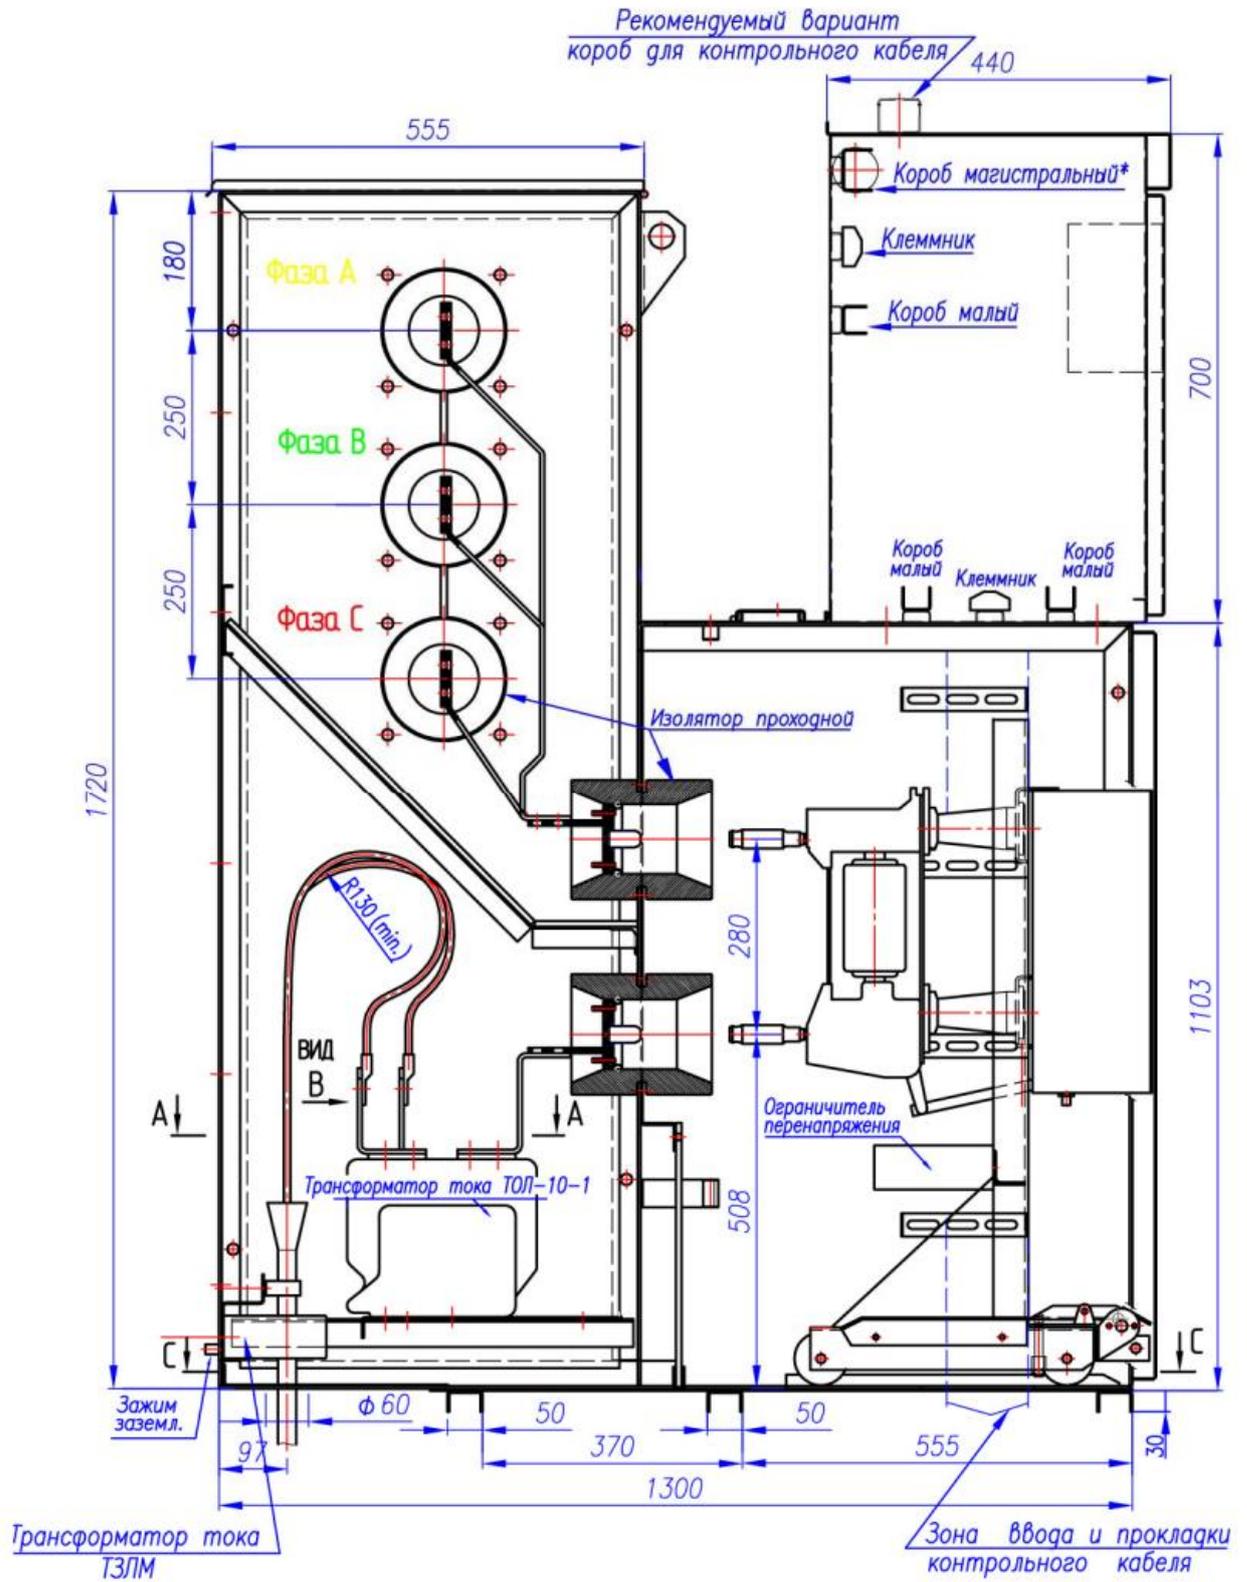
Габаритно-присоединительные размеры шкафа КМ-1КФ- с вакуумным выключателем до 1250 А
